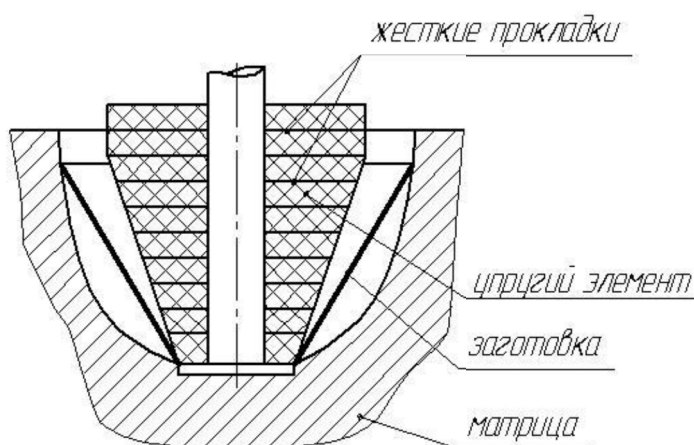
Процесс штамповки деталей эластичным инструментом
